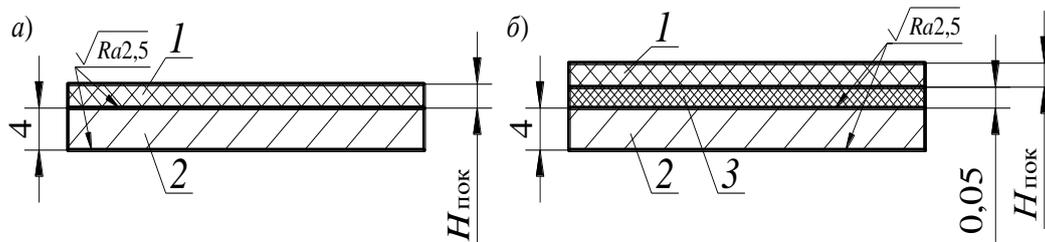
Образцы с напыленным ЛКП: а – образец с напыленным ЛКП на стальную пластину; б – образец с напыленным ЛКП на ПЭТ пленку; 1 – покрытие; 2 – стальная пластина; 3 – ПЭТ пленка
